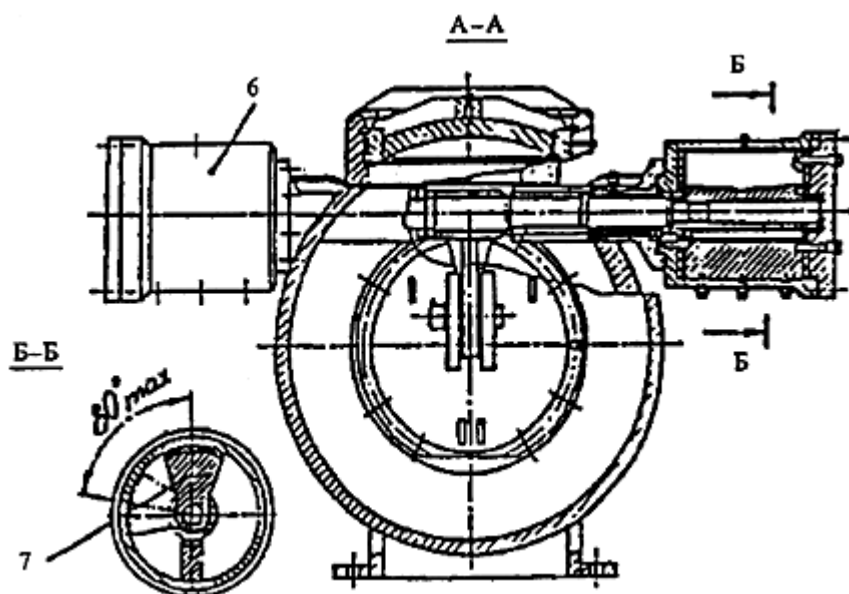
Обратный поворотный клапан с пневматическим демпфером:
